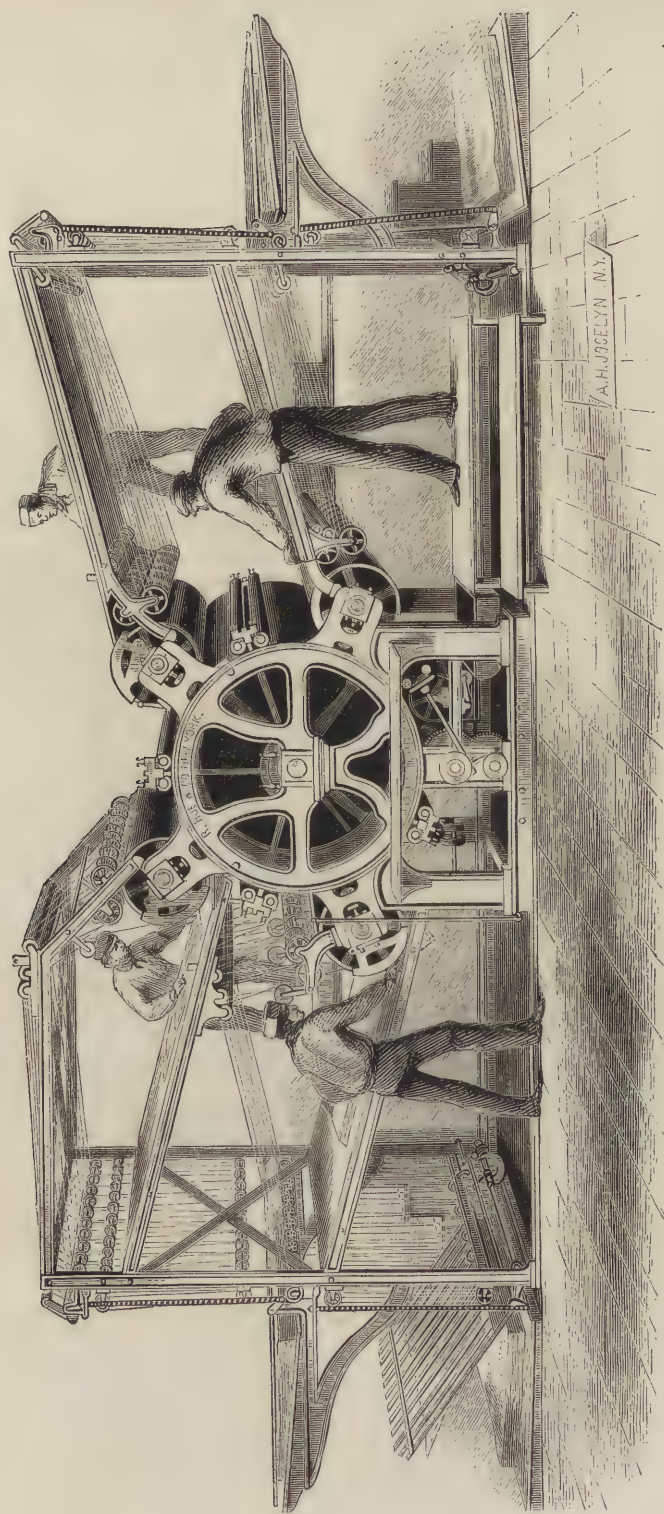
MACHINE CYLINDRIQUE A QUATRE MARGEURS.
